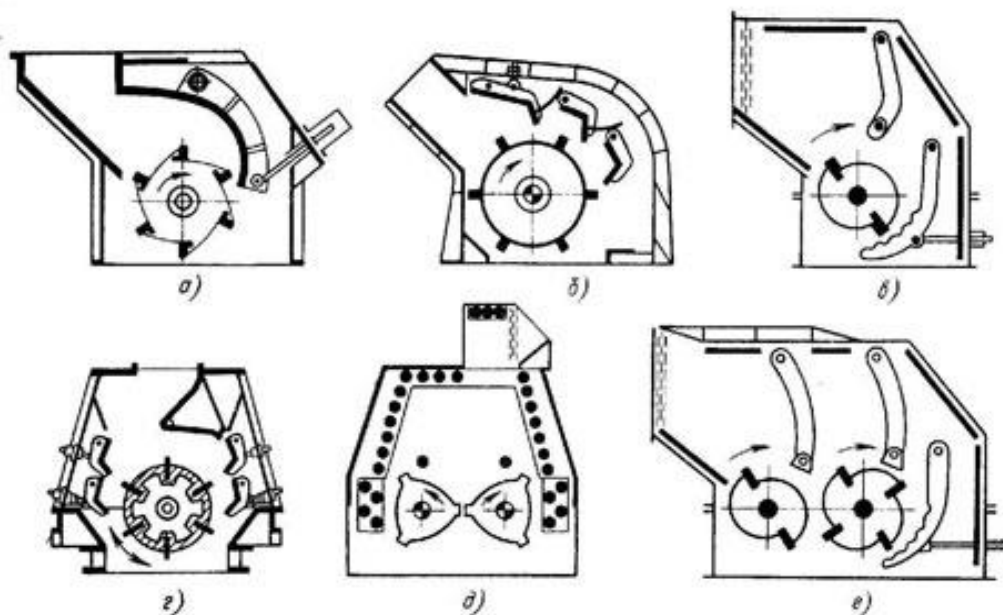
Конструктивные схемы роторных дробилок:
